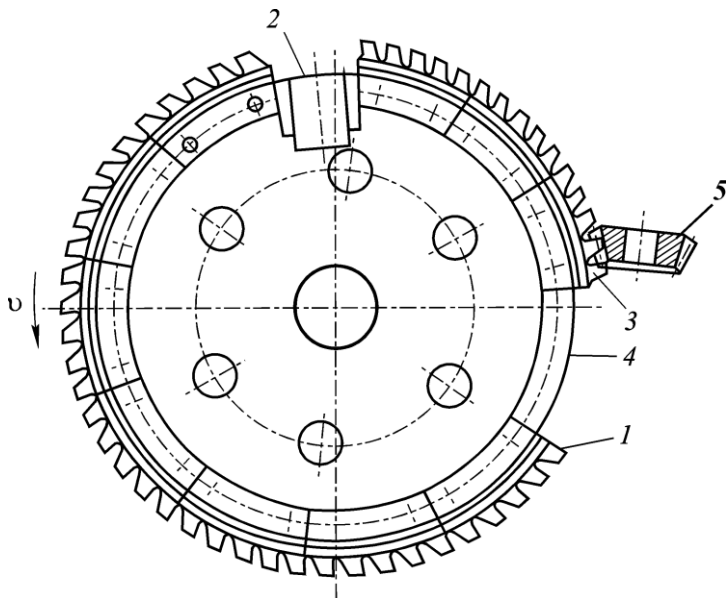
Схема нарезания конического прямозубого колеса круговой протяжкой
